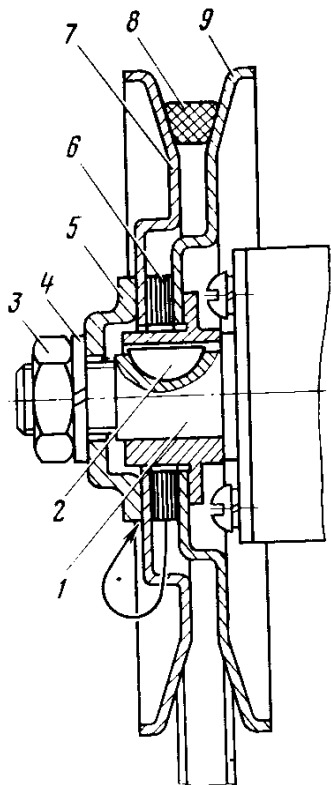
Устройство для натяжения ремня вентилятора: 1 — вал генератора; 2 — шпонка; 3 — гайка; 4 — шайба; 5 — нажимной колпачок; 6 — регулировочные шайбы; 7 — передняя половина шкива; 8 — ремень; 9 — задняя половина шкива
